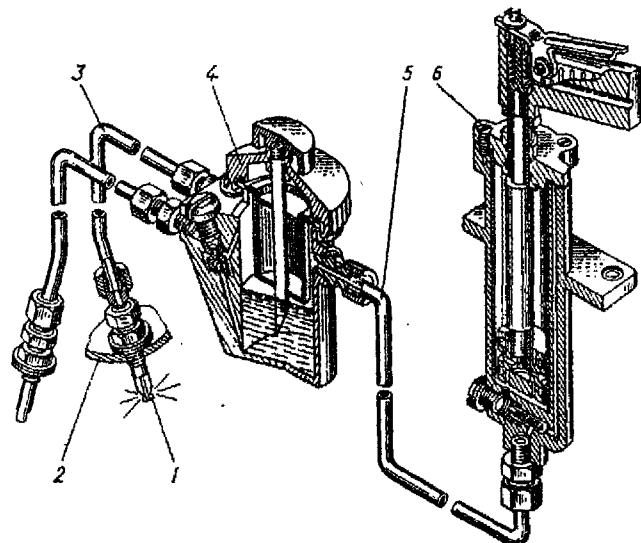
Пусковое приспособление 5ПП-40А: 1 – распылитель в сборе; 2 – впускной трубопровод; 3 – эмульсионная трубка; 4 – смеситель; 5 – воздушная трубка; 6 – насос
